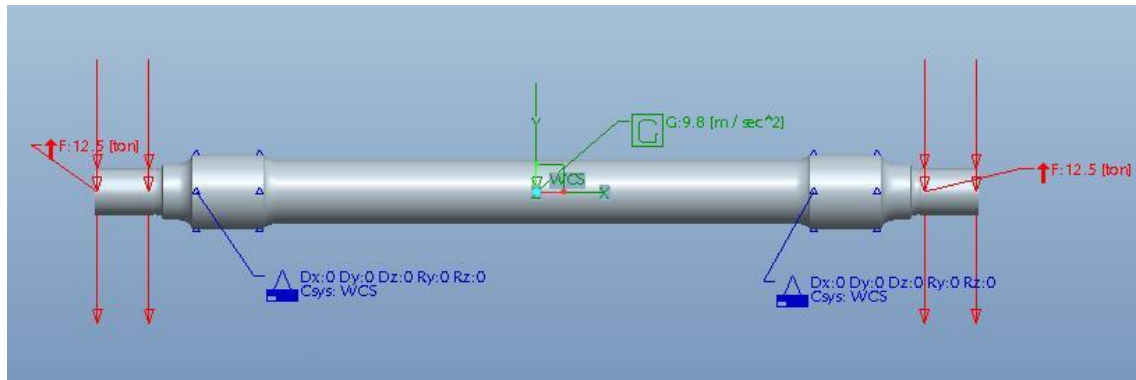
Eje finalizado con las cargas y restricciones definidas.
